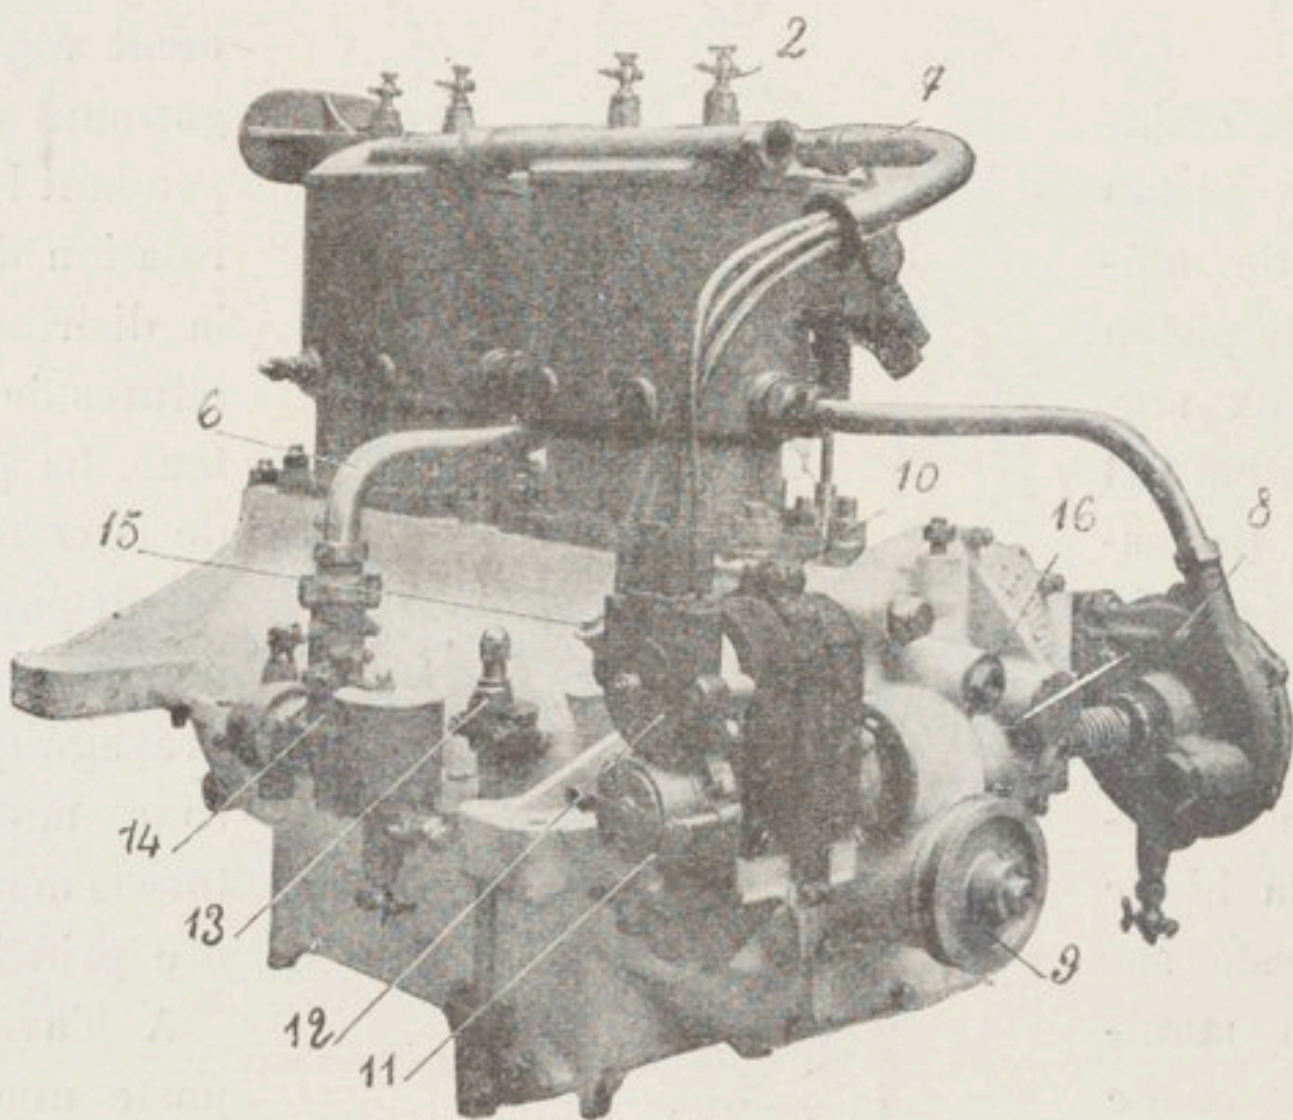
Vue d'ensemble du moteur d'automobiles à quatre cylindres de Dion-Bouton.
